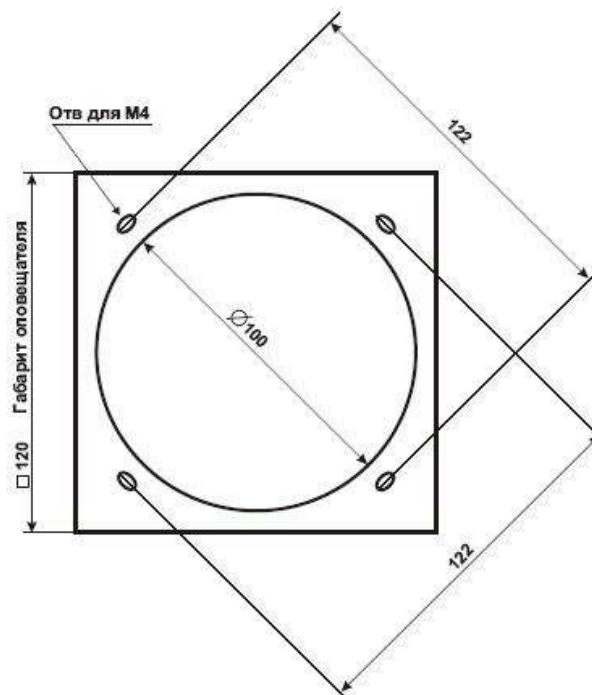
Габаритные размеры монтажной пластины SMP и размеры потолочных отверстий для установки оповещателей.
